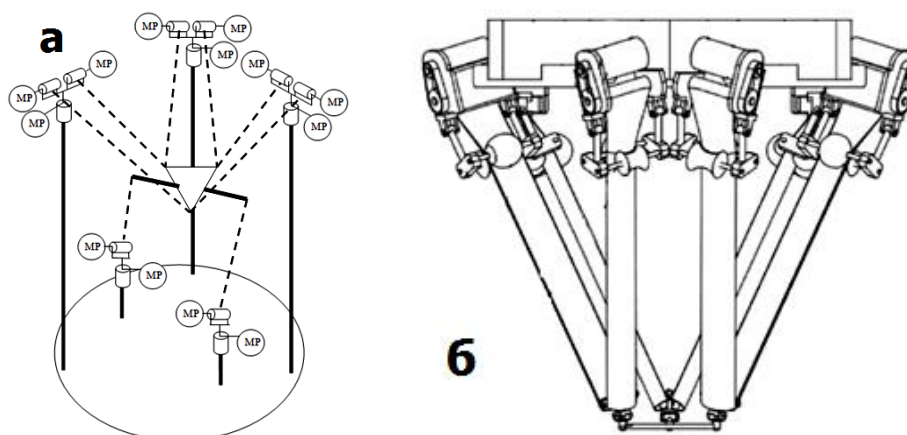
Механизмы с ременными и тросовыми приводами [1, 2]: МР - мотор-редуктор.
